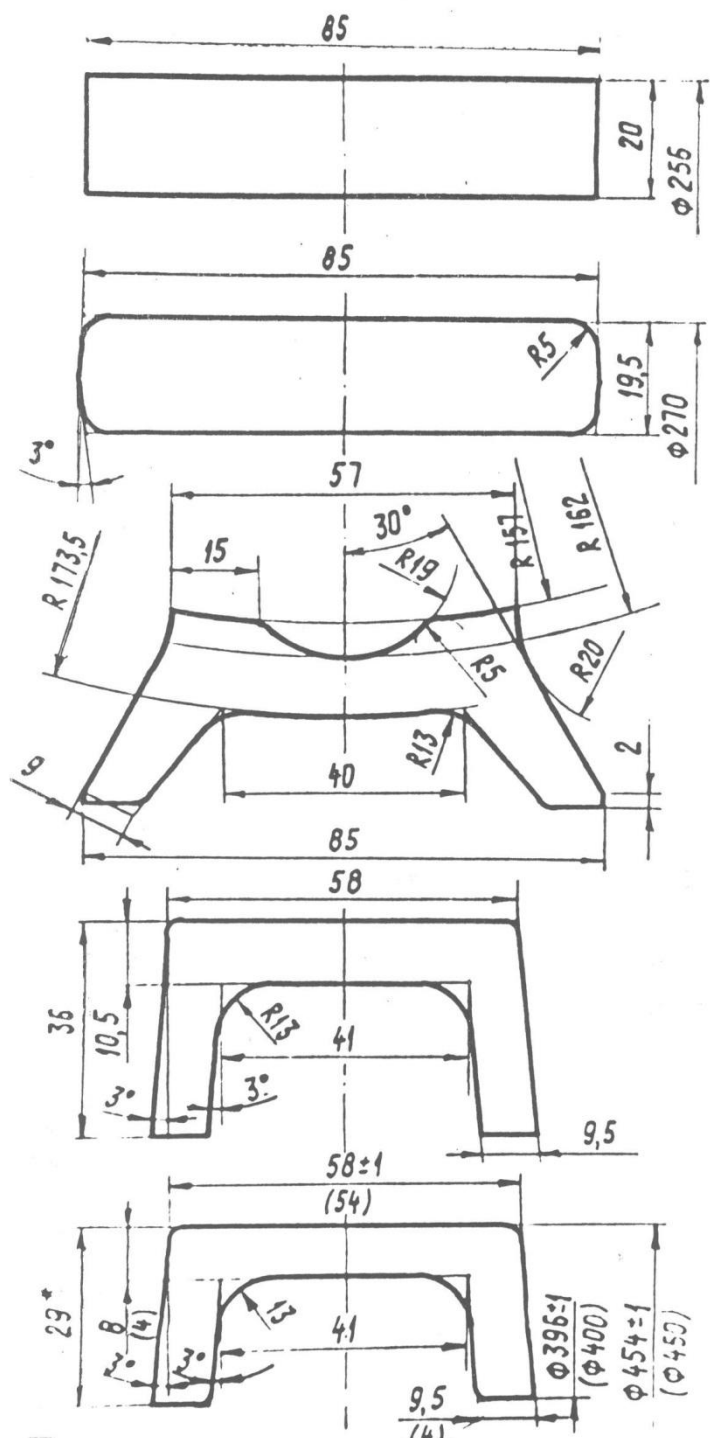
Калибровка заготовки промежуточного кольца дисков из сплва
